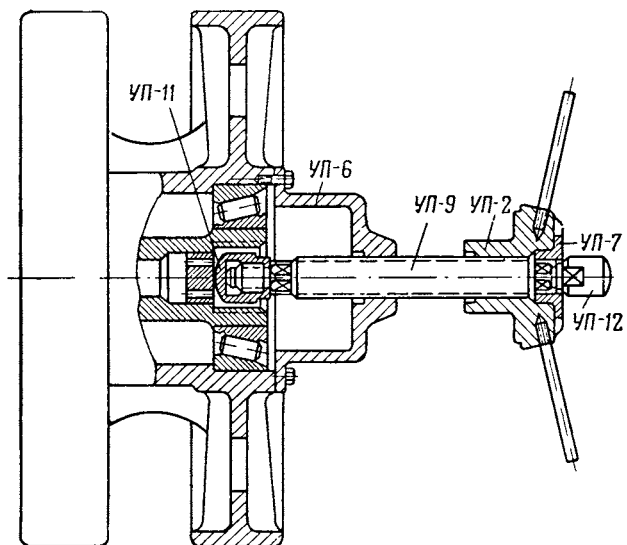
Универсальное приспособление 48001-1-074 УП, снятие направляющего колеса и опорного катка
